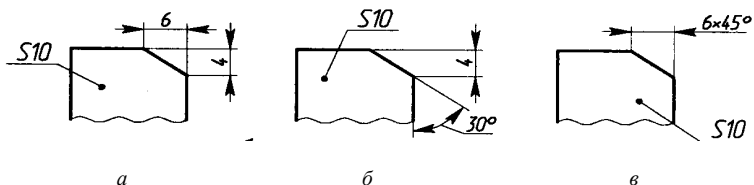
Простановка размеров фасок: *а* – двумя линейными размерами; *б* – одним линейным и угловым размером; *в* – комбинированным способом
